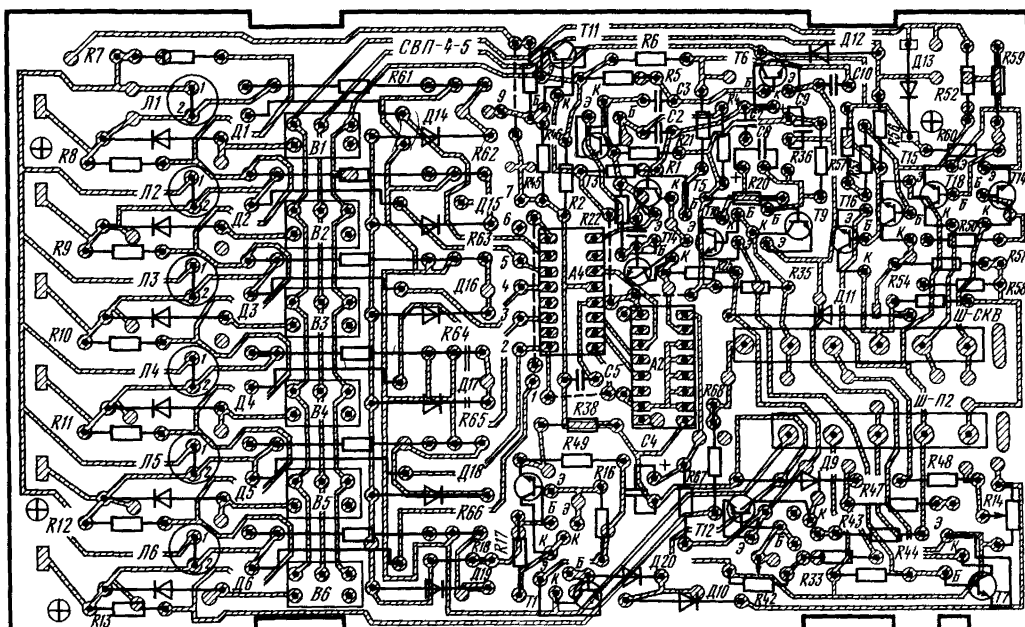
Электромонтажная схема печатной платы СВП-4-4 – СВП-4-7
